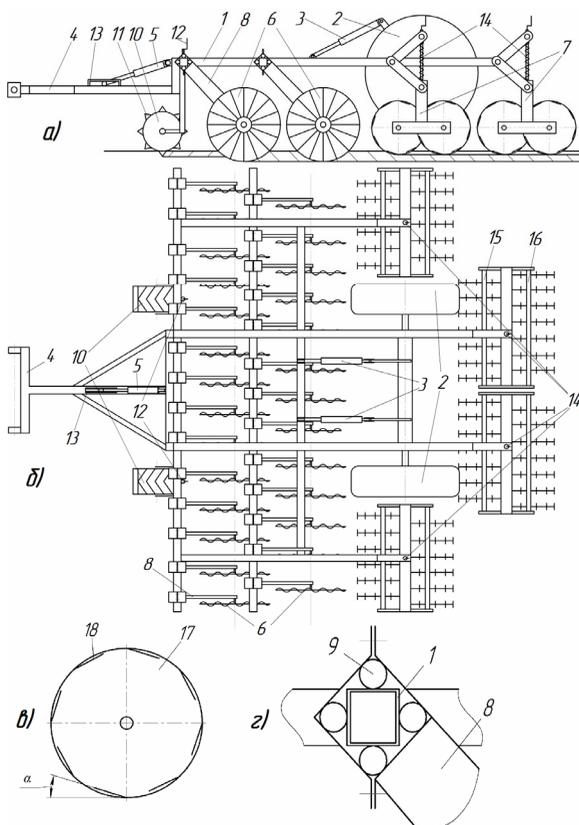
Схема агрегата для предпосевной обработки почвы в системе почвозащитного земледелия: а – агрегат, вид сбоку; б – агрегат, вид сверху; в – прикатывающий рабочий орган; г – защита стоек турбодисков на упругих элементах, 1 – рама; 2 – транспортные колеса; 3, 5 – гидроцилиндр; 4 – прицепное устройство; 6 – турбодиск; 7 – прикатывающие рабочие органы; 8 – стойка; 9 – упругий элемент; 10 – опорные колеса; 11 – рыхлитель; 12 – винтовой механизм; 13 – паз
